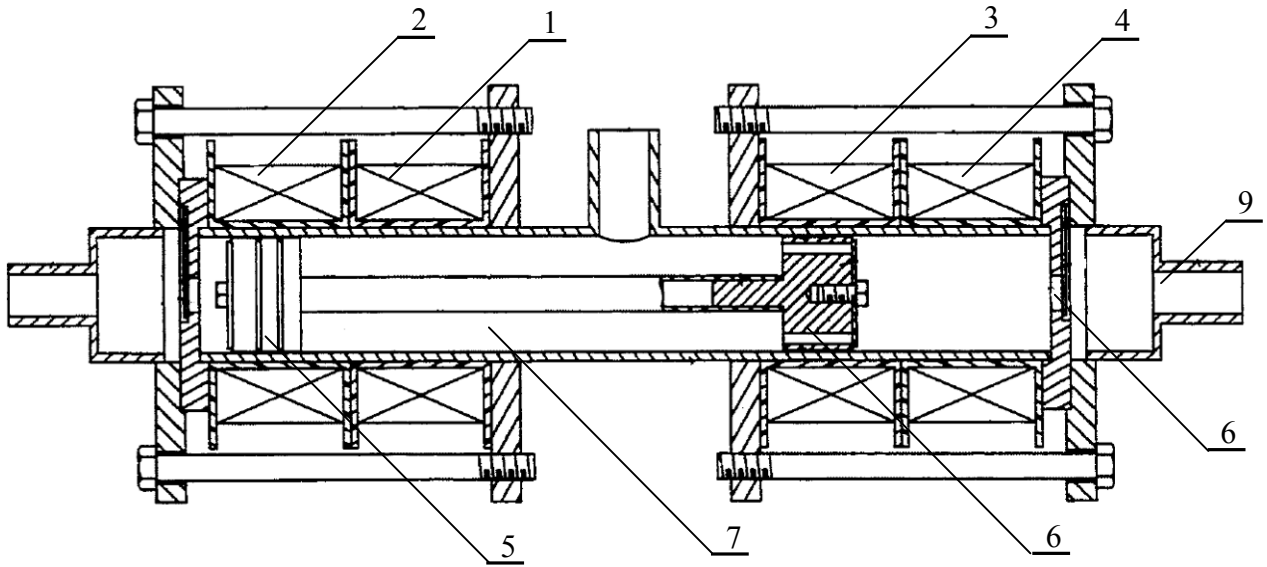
Двухсторонний электромагнитный компрессор
